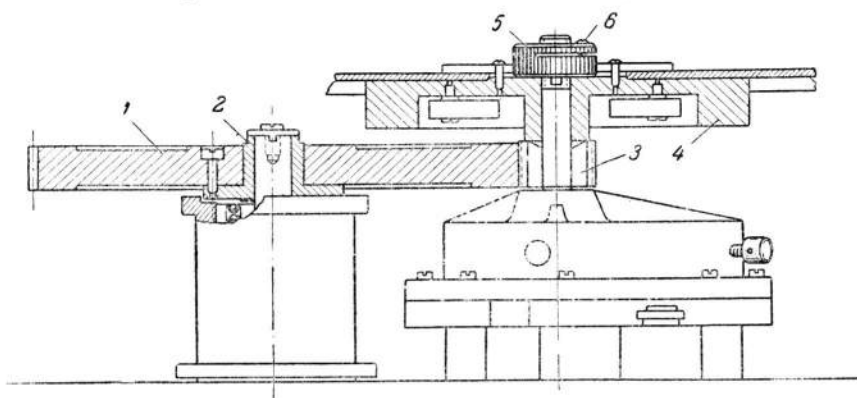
Крепление текстолитовой шестерни на валу комбинированного барабана и малой шестерни с маховиком на валу эксцентрика
